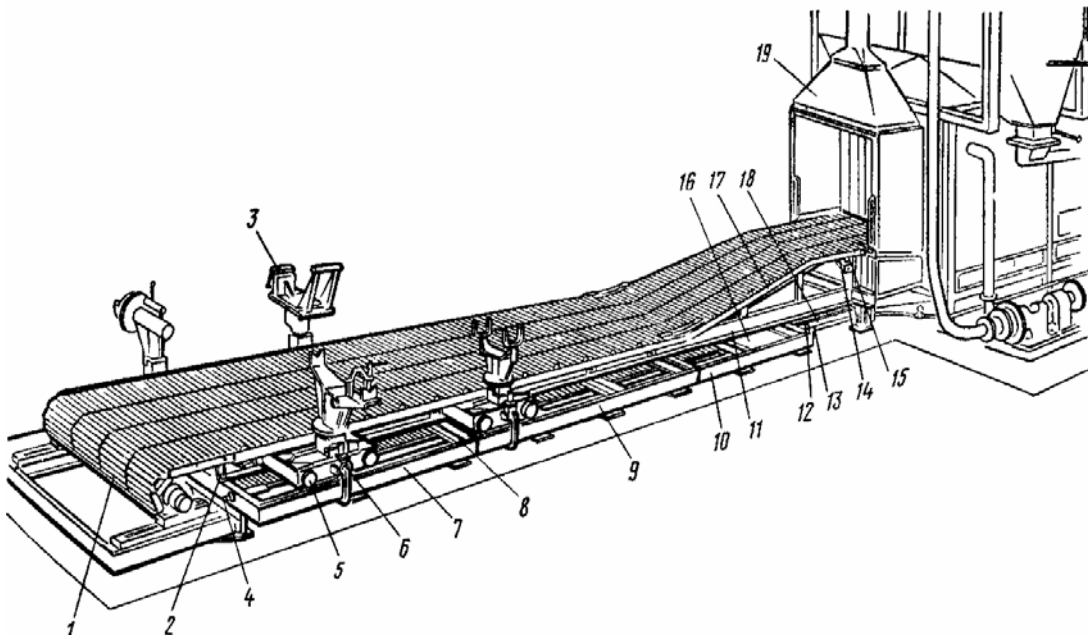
Конвейер с пластинчатым транспортером для разборки автомобильных агрегатов: 1 – транспортер; 2 и 12 – упоры; 3 – разборочный поворотный стенд; 4 – натяжное устройство; 5 – тележка; 6 – винтовой зажим; 7 – рама; 8, 11, 17 и 18 – направляющие; 9 и 10 – секции; 13 – патрубков; 14 и 15 – конечные выключатели; 16 – поддон; 19 – очистная струйная машина.
